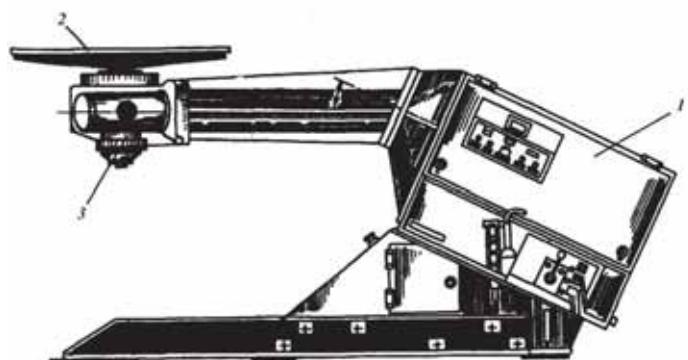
Сварочный позиционер: 1 – корпус; 2 – рабочий стол; 3 – привод стола
